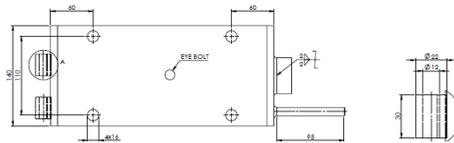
Insert Cetakan Aluminium kedalam Plat Besi
